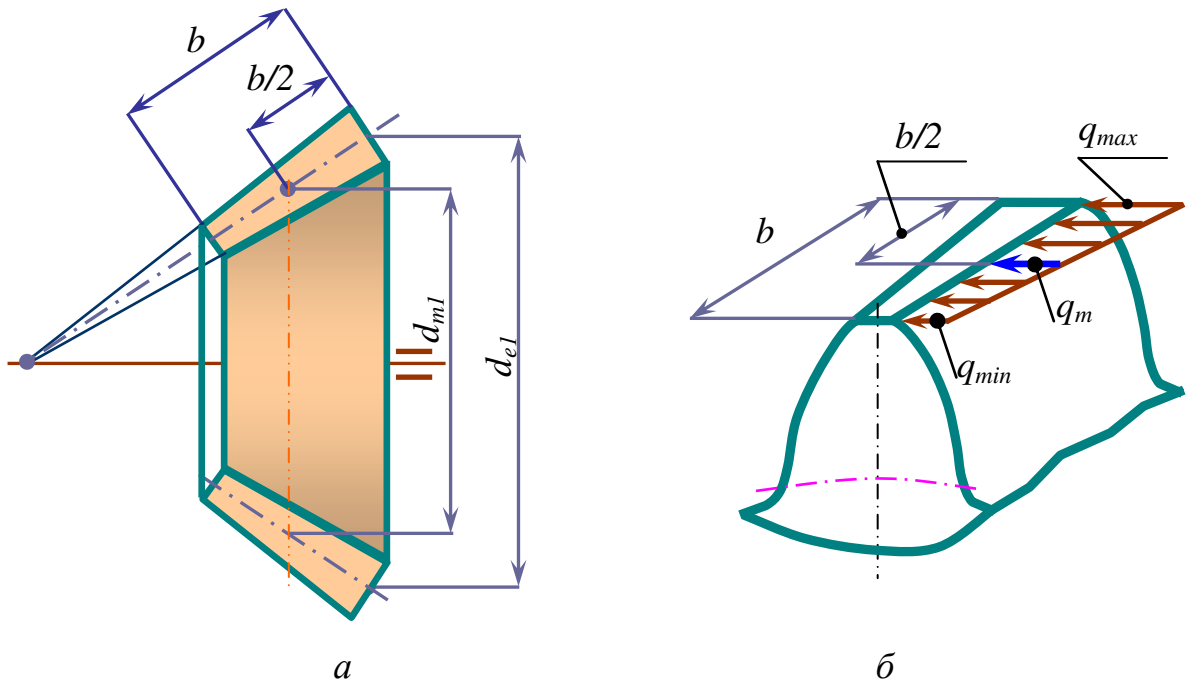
Схема построения эквивалентного цилиндрического зубчатого колеса
